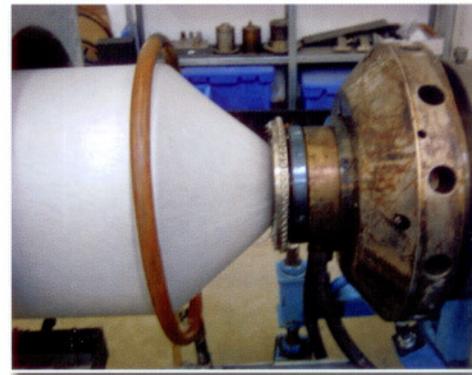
采用圆形柔性环模头生产发泡片材的生产线 / Fig. 6 Line which produces foamed sheets using a circular Flex Ring die
